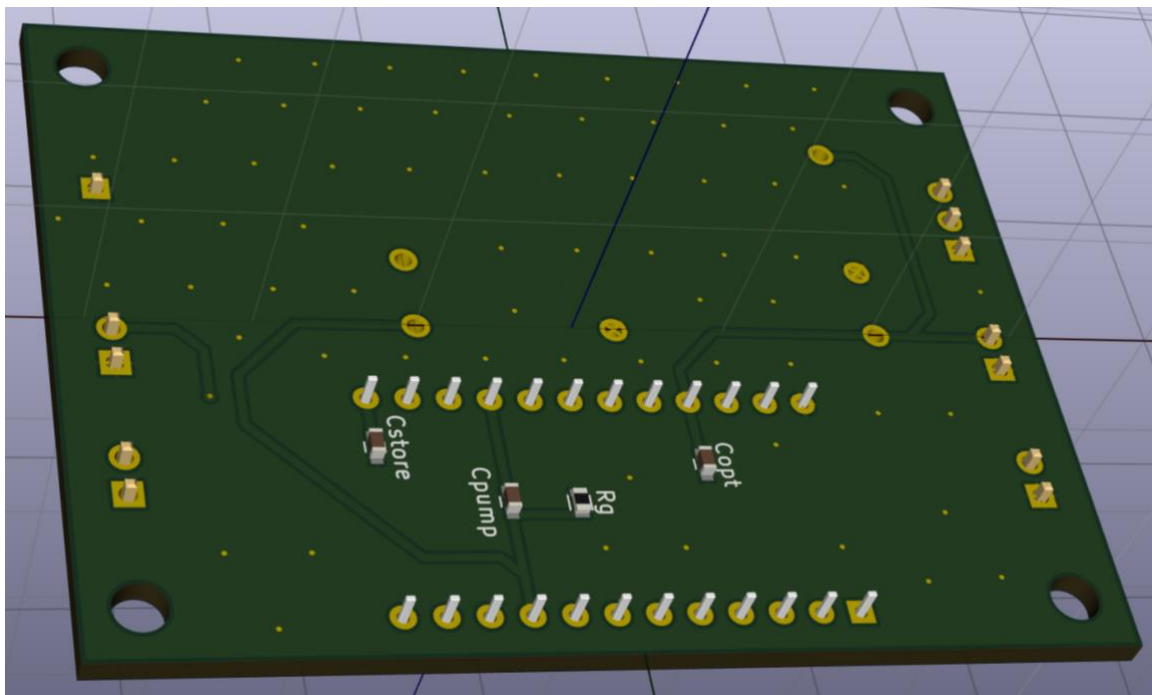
Visualizzazione 3D strato inferiore primo PCB
